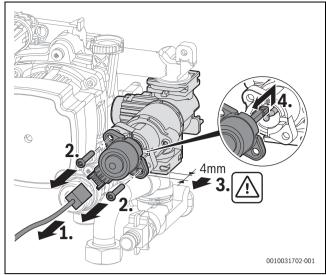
Separar el motor de la válvula de 3 vías (variante con tornillos) Instalar el motor.
